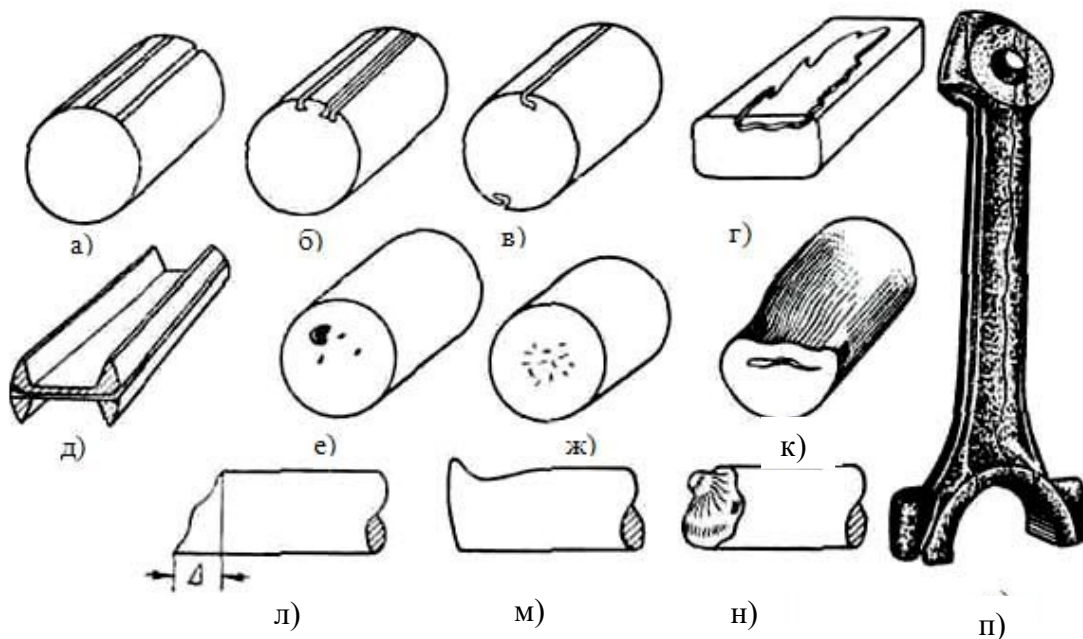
Види браку вихідного матеріалу та заготовок
